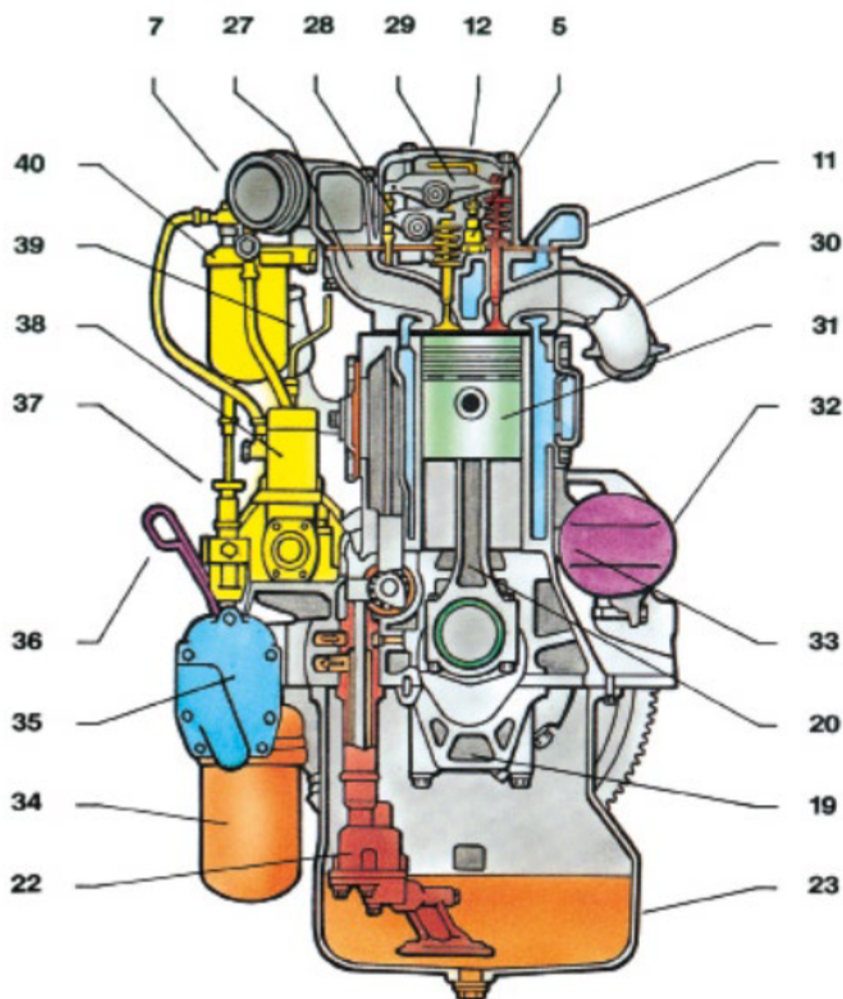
Vista frontal dos componentes de um motor de combustão interna.
